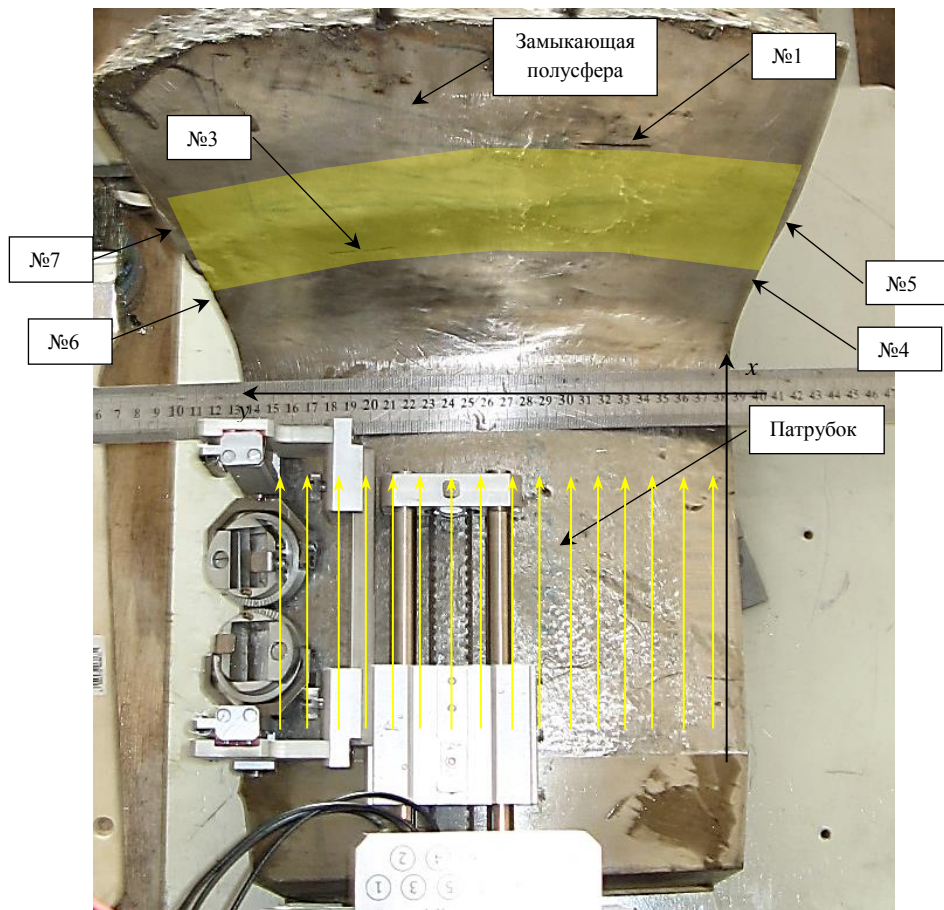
Фотография испытательного образца. Контуры сварного соединения схематически показаны полупрозрачным многоугольником жёлтого цвета
